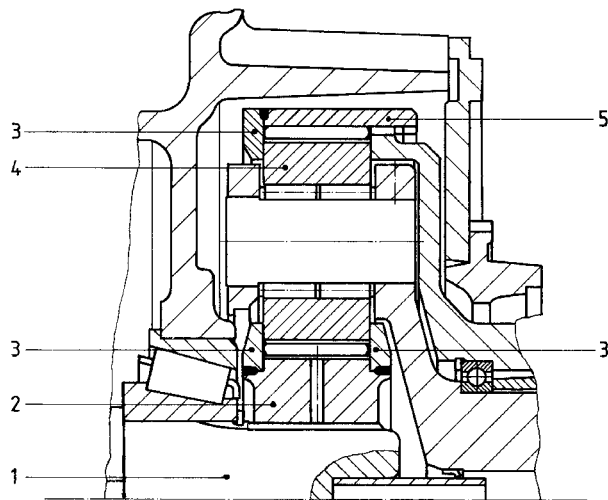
Druckkammeinsatz im Planetengetriebe mit Schrägverzahnung; 1) Hauptwelle; 2) Sonnenrad; 3) Druckkämme bzw. Axialkraftaufnahme mittels Anlaufringen; 4) Planetenrad; 5) Hohlrad /5/
